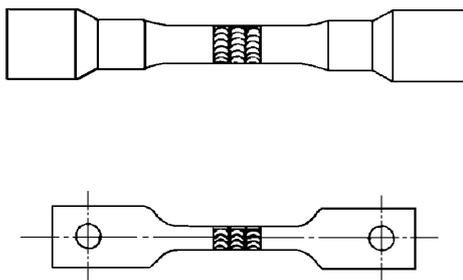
Cordon de soudure déposé sur un barreau
